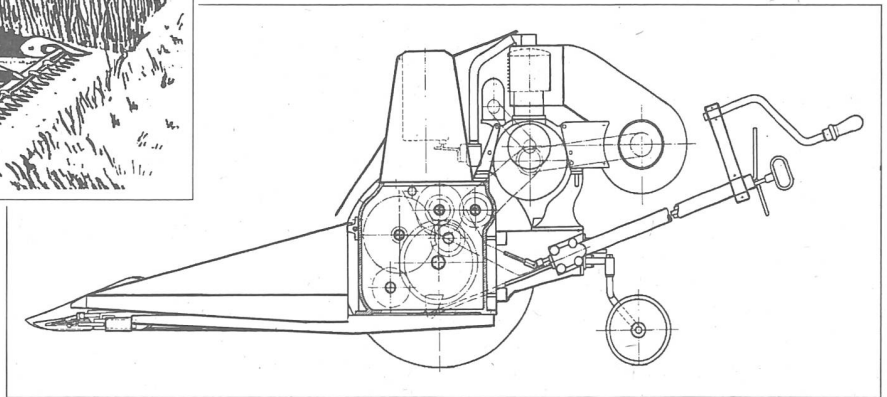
Schnitzzeichnung durch den ersten Rapid-Motormäher, dessen Grundprinzip viele Nachahmer fand. Weltweit wurden seither gegen eine Million Motormäher gebaut.
